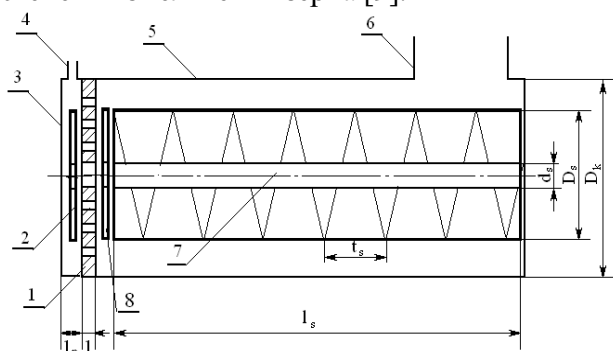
Принципиальная схема машины для приготовления полужидких концентрированных кормов: 1 - неподвижный нож; 2 - подвижный нож, выполняющий одновременно функции центробежного насоса; 3 - корпус подвижного ножа; 4 - выходное отверстие для смеси измельченного зерна и воды; 5 - корпус шнека; 6 - загрузочное отверстие для смеси неизмельченного зерна и жидкости; 7 - вал шнека; 8 - подвижный нож шнека
